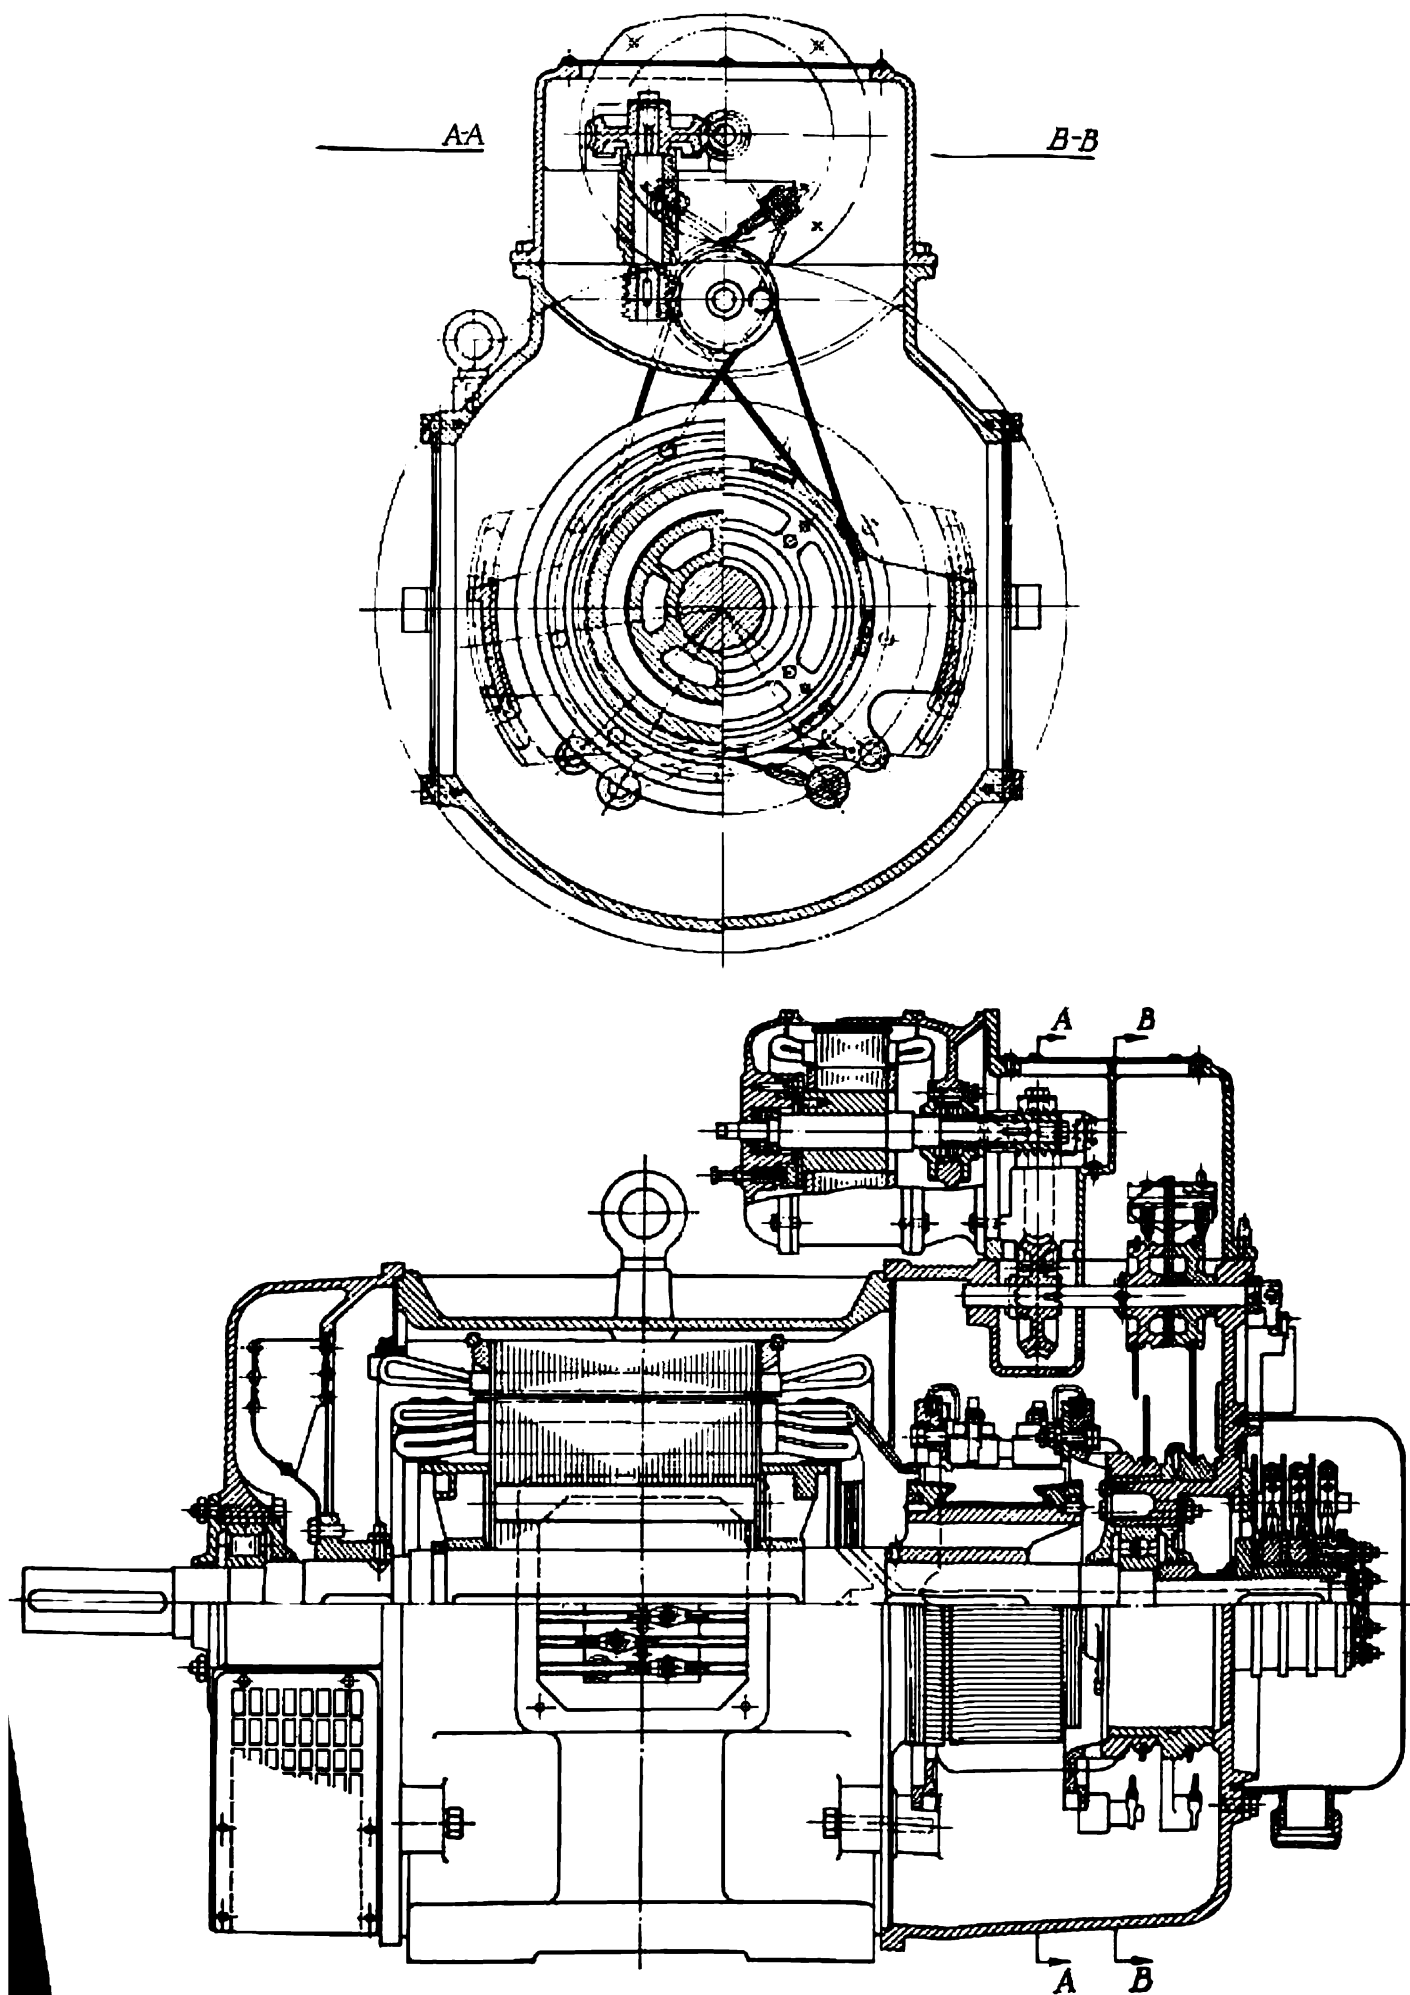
Coupe d'un moteur à collecteur Schrage-Richter.
